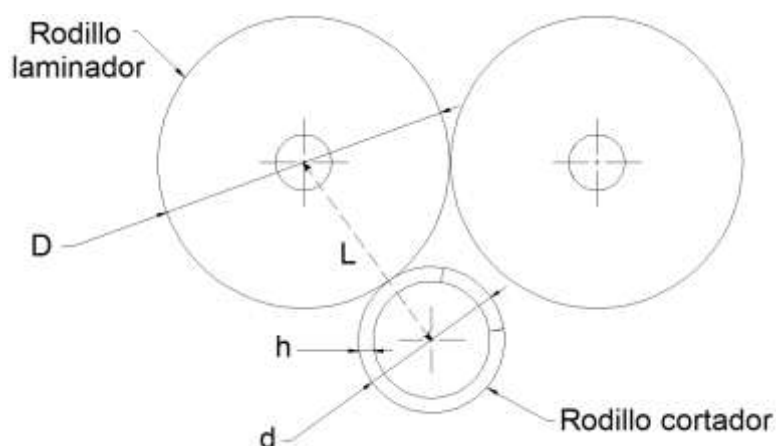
16 Esquema del conjunto rodillo laminador-cortador
